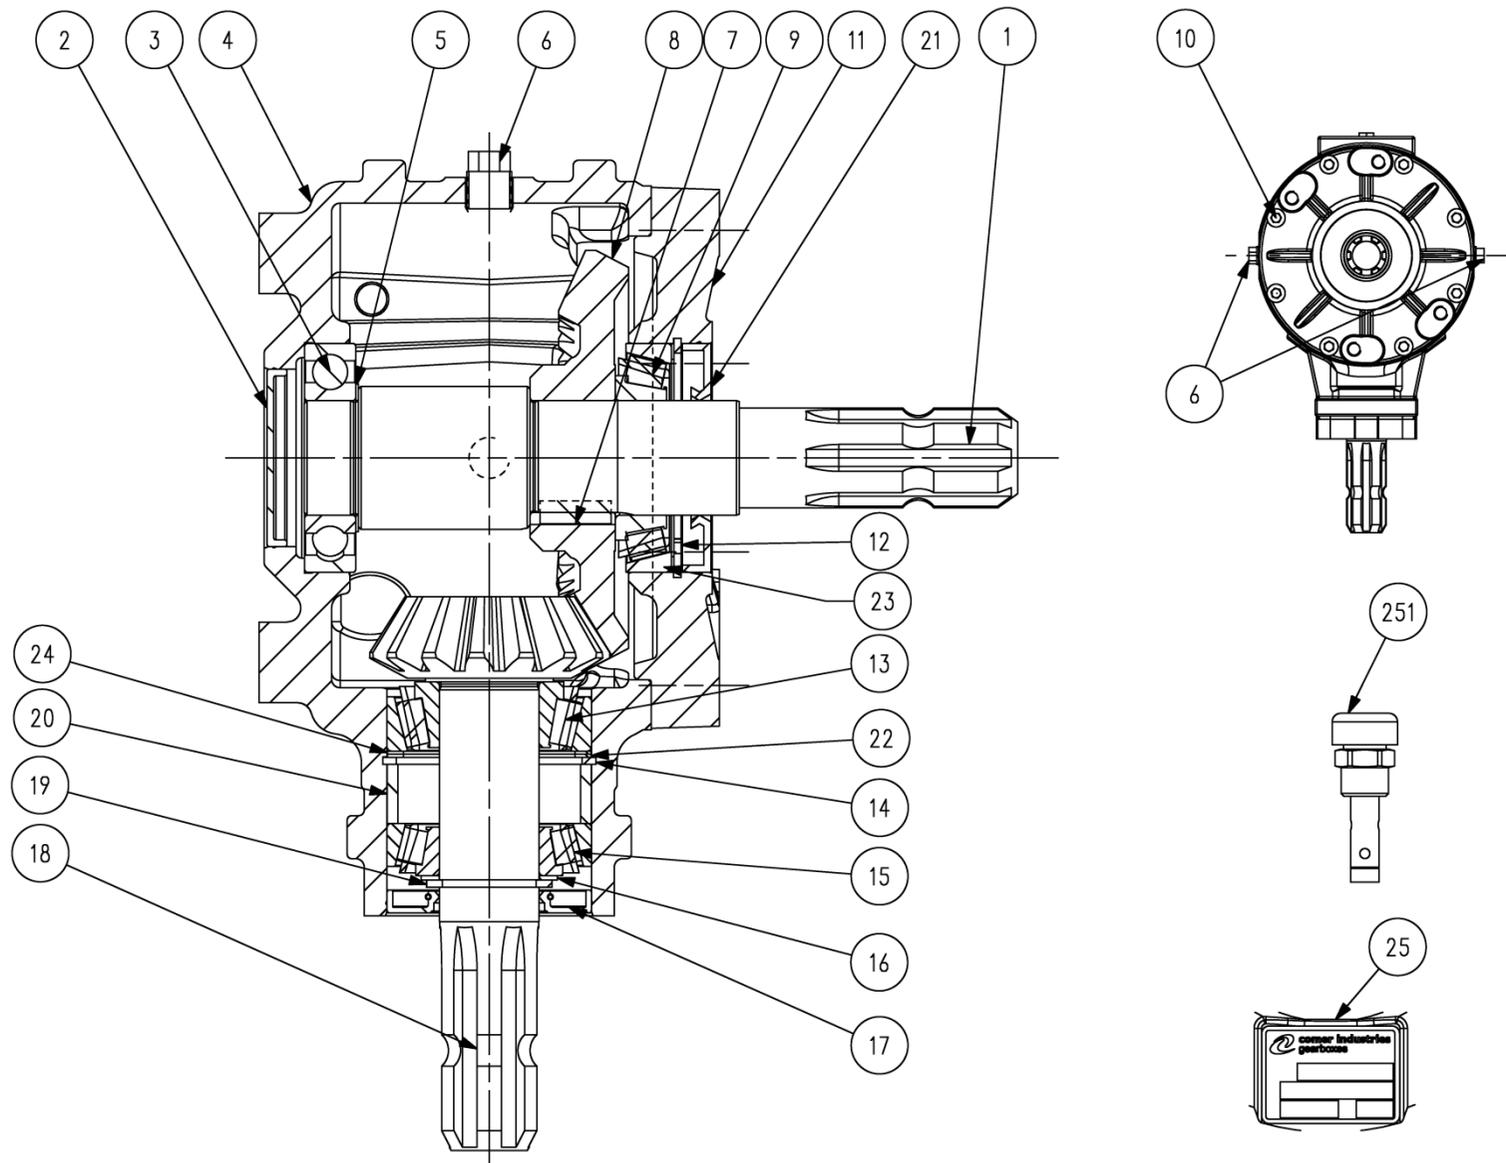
Редуктор 9.304.521.10 "Comer industries"
